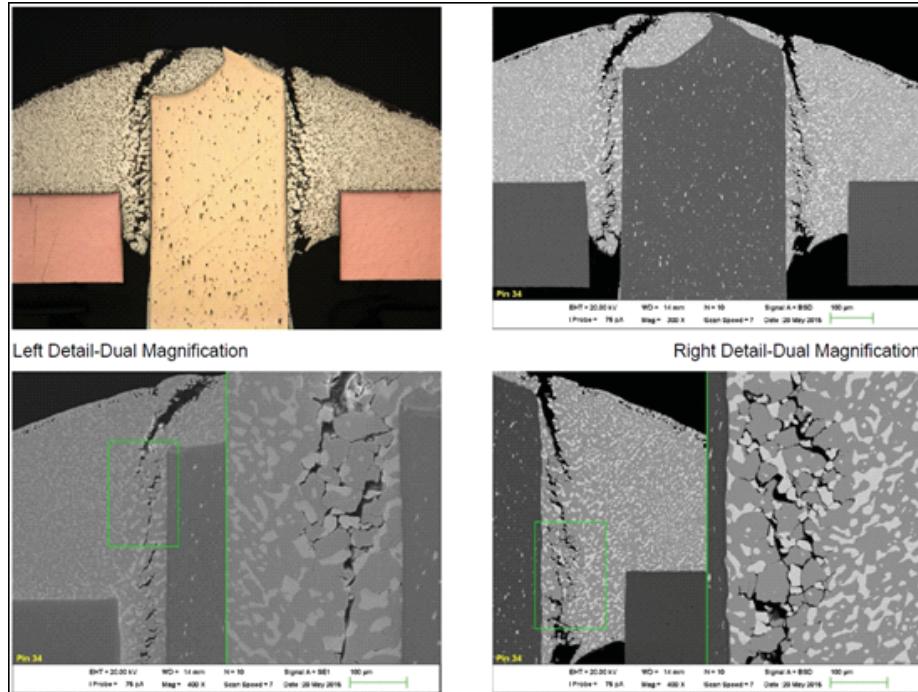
Pin 34 焊接點切片影像
